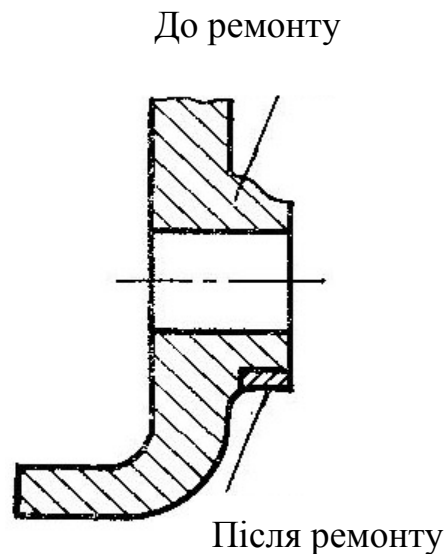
Схема установки бандажів для відновлення обломаної бобишки корпусних деталей
